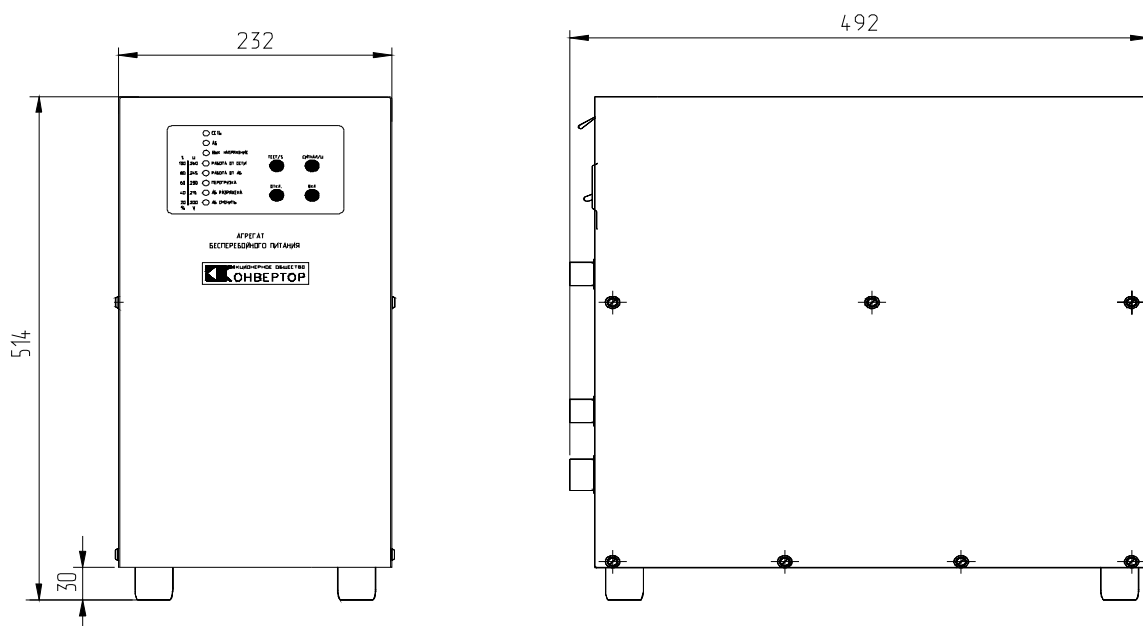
Габаритный чертеж АБП-ООПТ-8.
